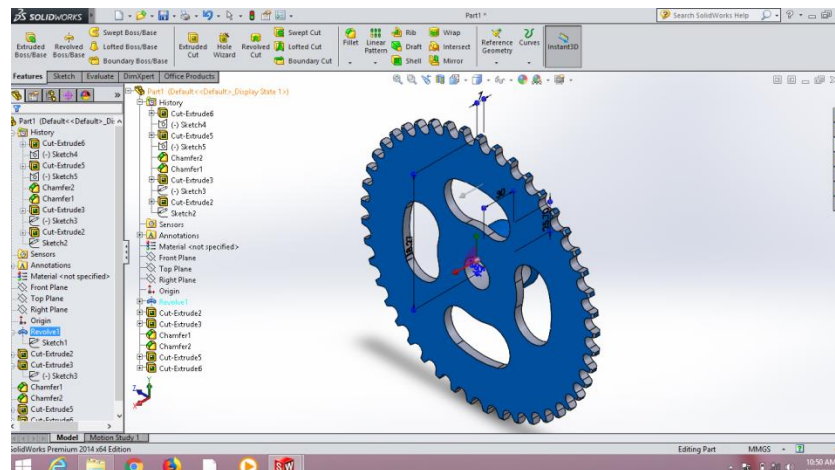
Gambar awal 3 dimensi sprocket besar
